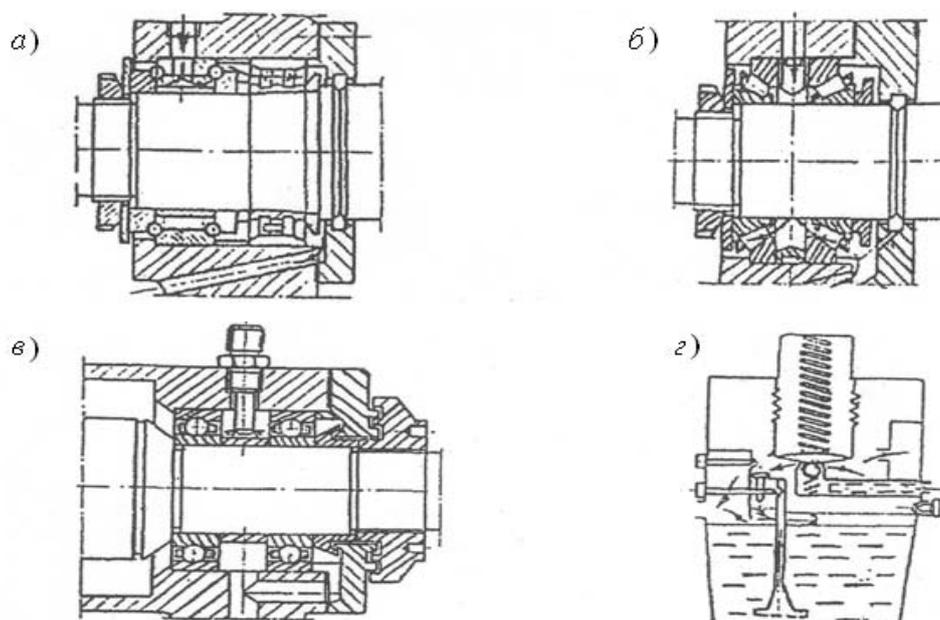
Схемы смазывания подшипников шпиндельных опор
